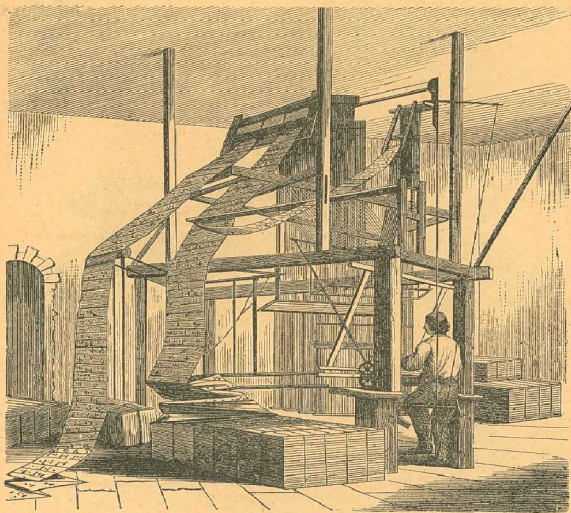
Conjunto de machina de tecer, de Jacquard
